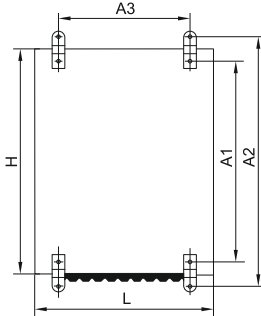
Вид корпуса сзади / Figure 1 – Enclosure back elevation / 1 сурет – Корпустың артқы көрінісі
